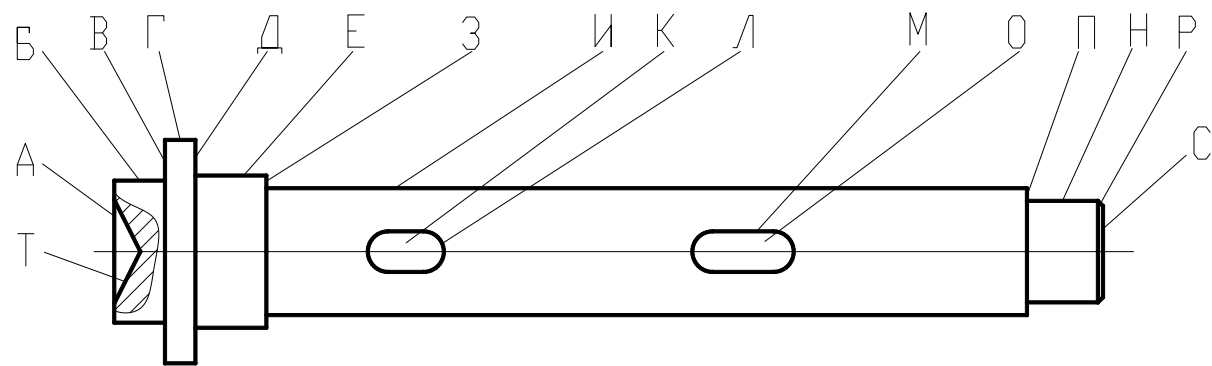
Ескіз валу вузла приводу машини марки МНТР-130/600 з позначеними оброблюваними поверхнями.
